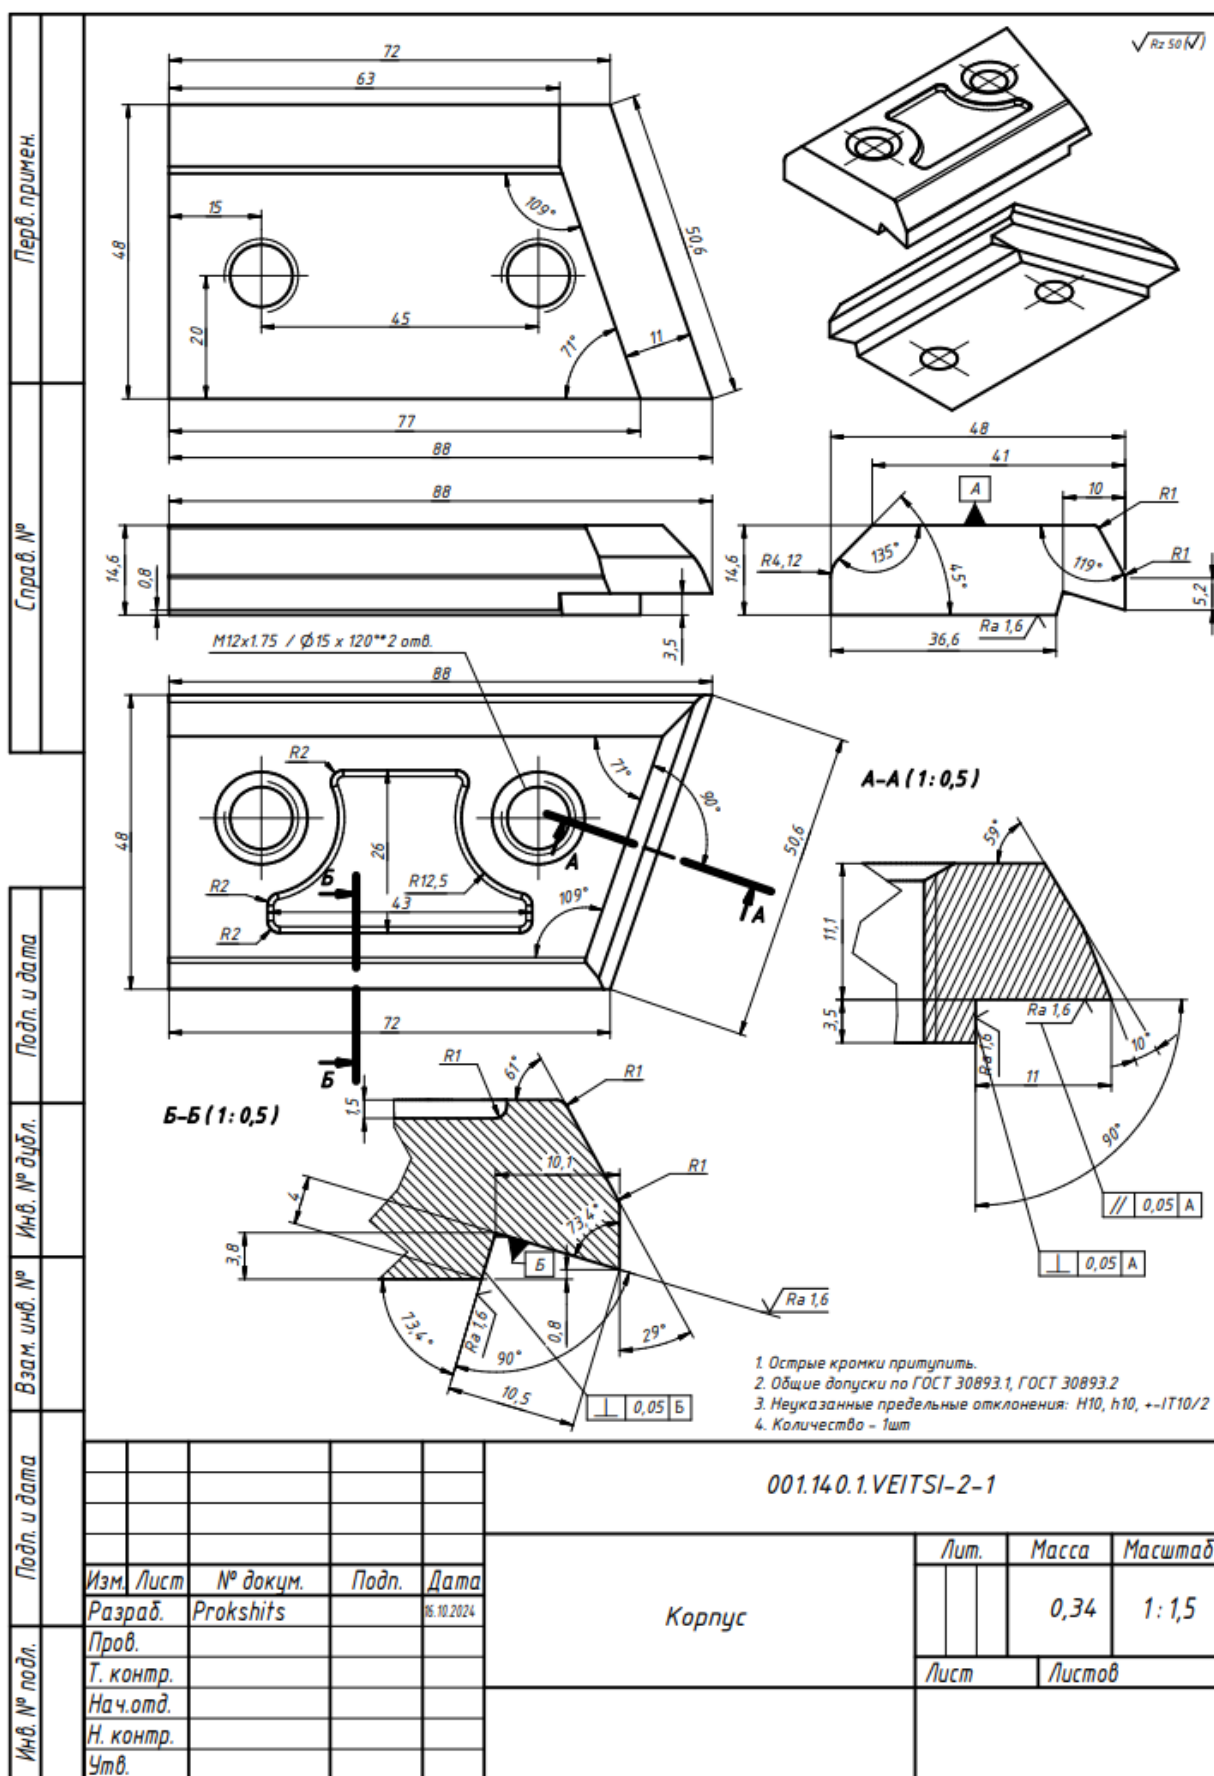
Чертеж корпуса сменного лезвия короснимателя
